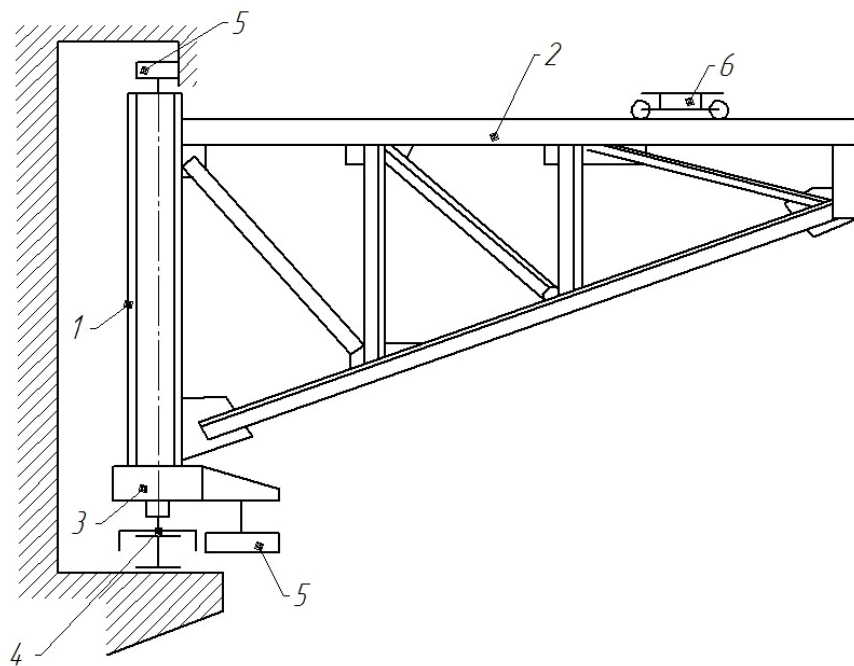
Настінний консольний кран з їздою "по верху"
